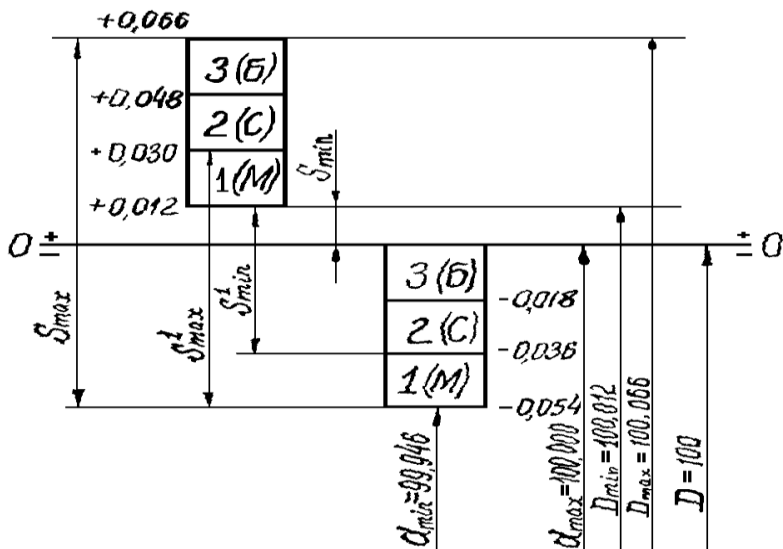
Соединительные детали схемы поля допусков $\varnothing 100 \frac{G8}{h8}$, которое классифицировано по трехмерным группам
